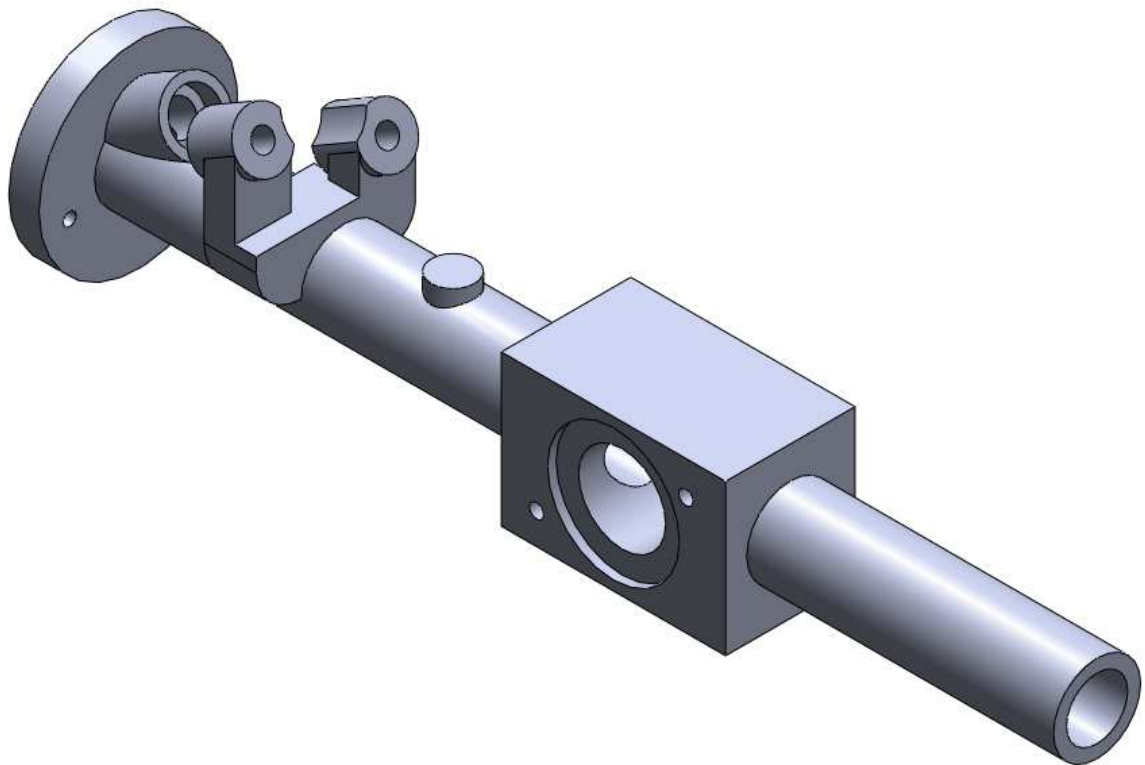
Bloco para fixação do sensor de posição e passagem do eixo da borboleta.
